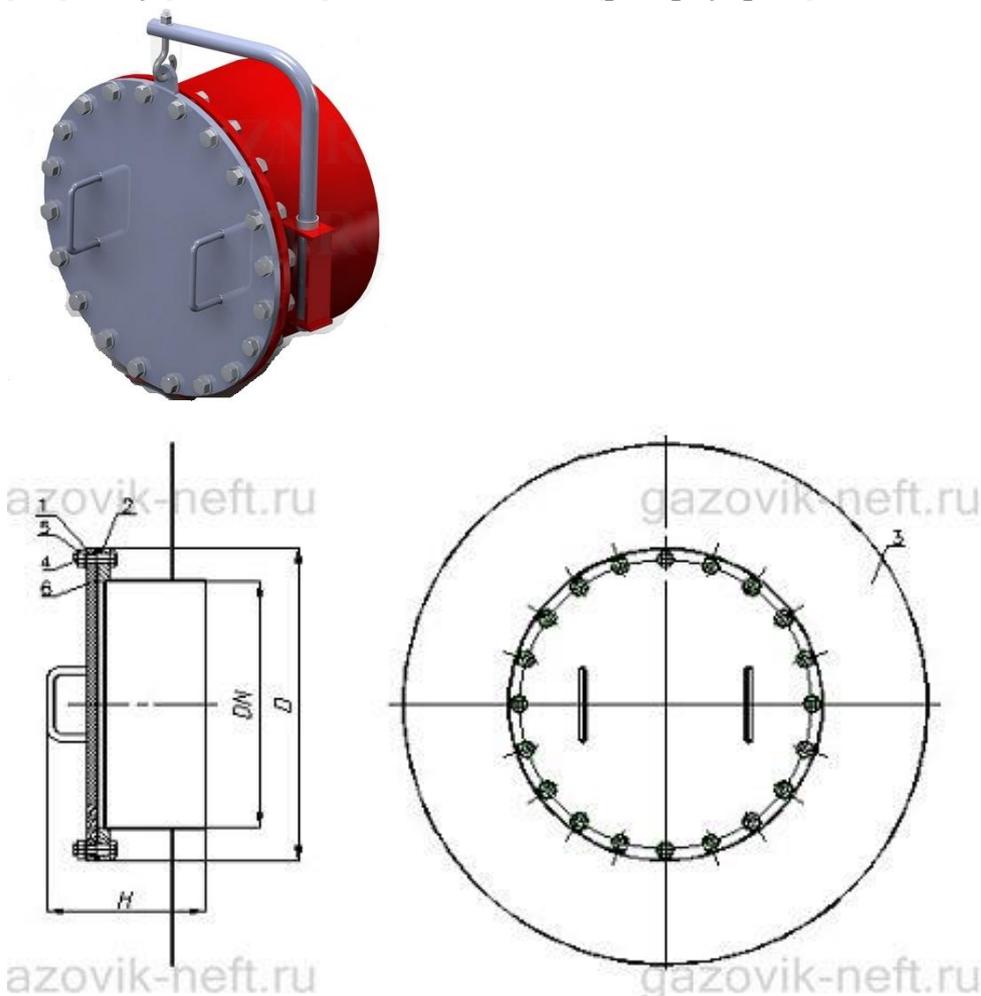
Люк лаз ЛЛ-500. Изображение (сверху) и общий вид (снизу), [163]: 1 – фланец; 2 – корпус; 3 - усиливающая накладка; 4 – болт; 5 – гайка; 6 – прокладка
